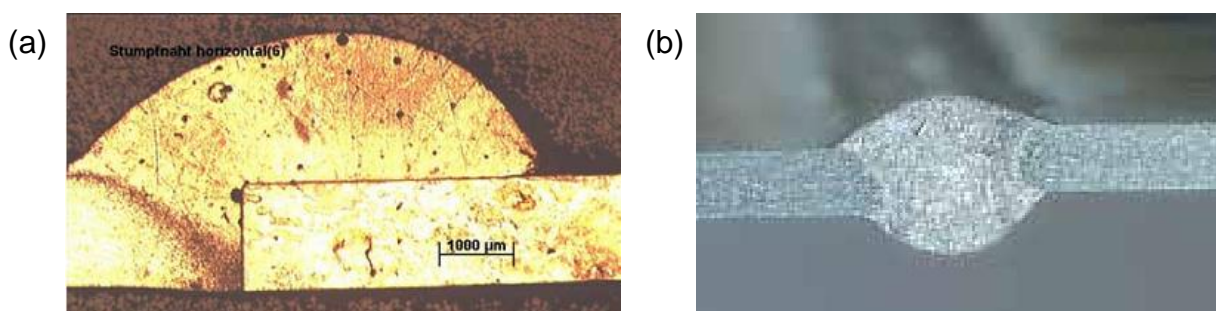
Soldagem com processo CMT (a) em junta de topo em chapas de alumínio de 0,8 mm, e (b) união de aço galvanizado com alumínio (ambós 1 mm de espessura), com velocidade de soldagem de 70 cm/min (Himmelbauer, 2005).
